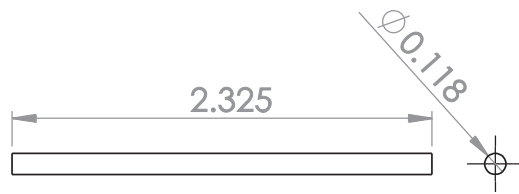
Dimensiones de la varilla que va dentro del tubo piezoeléctrico.
